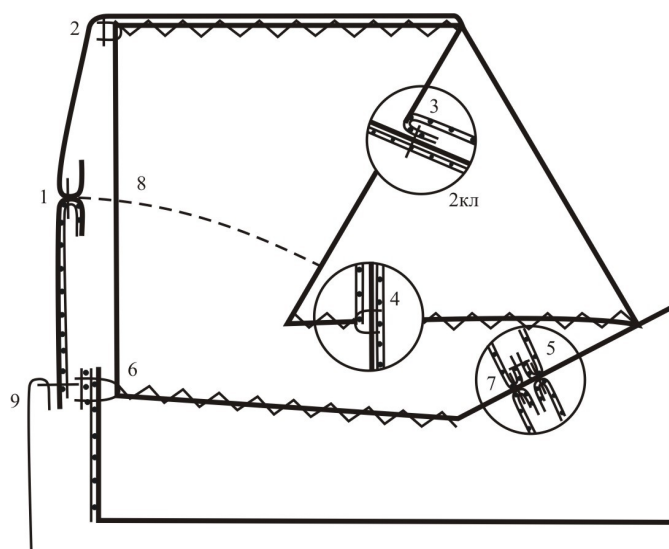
Сборочный чертеж воротника пиджачного типа
